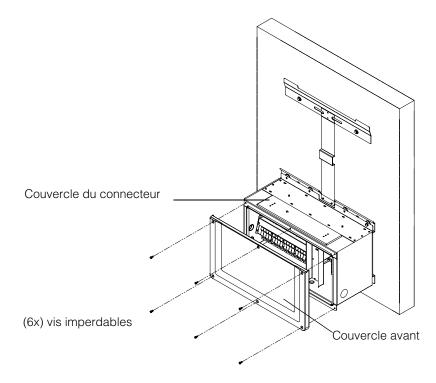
Ouverture du couvercle avant du boîtier de câblage
